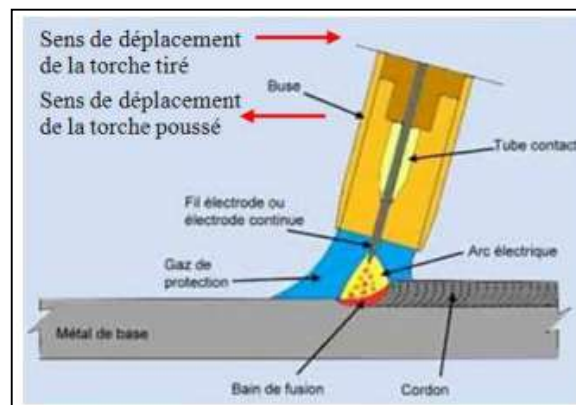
Procédés de soudage MIG/MAG [1]
